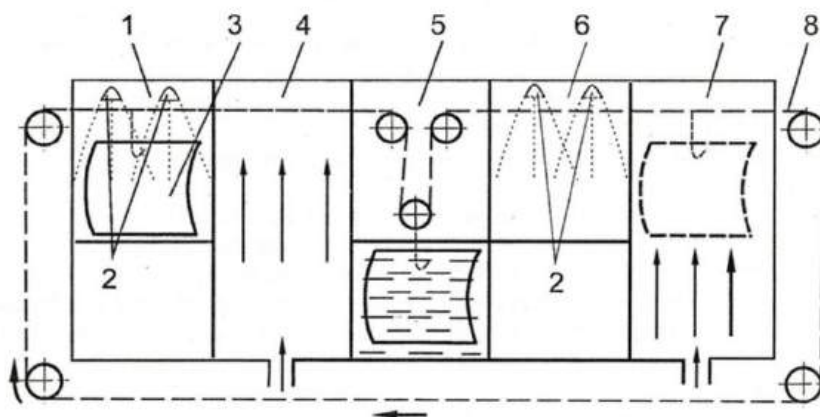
Схема хімічного оброблення обшивок: 1 – камера знежирення; 2 – розпилювач; 3 – обшивка; 4,7 – сушильна камера; 5 – ванна травлення; 6 – камера промивання; 8 – транспортер
